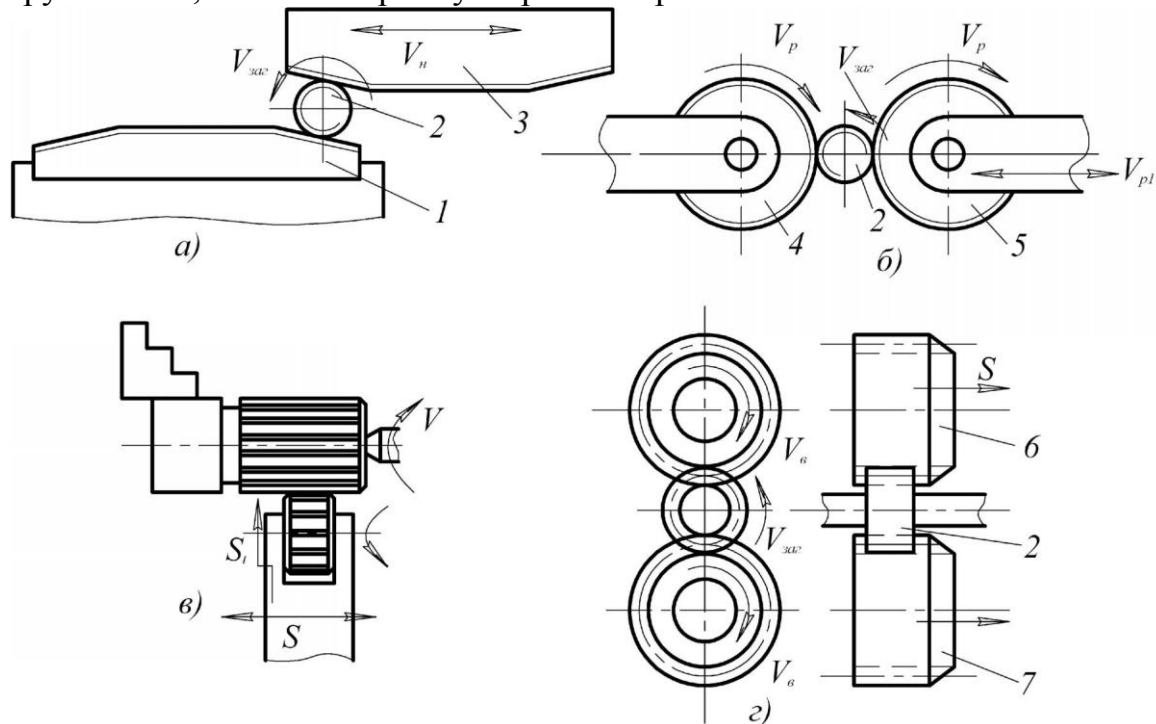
Схеми формуювальних методів обробки пластичним деформуванням
